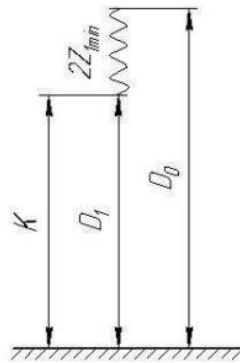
Размерные цепи при обработке наружной поверхности Ø22h11
